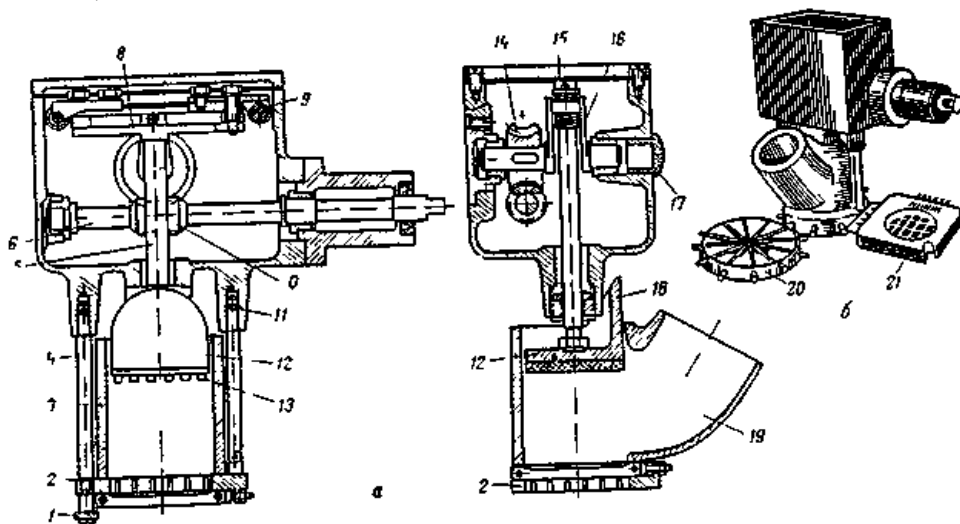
Механизм МС28-100 для нарезки сырых овощей: а — разрез; б — общий вид
